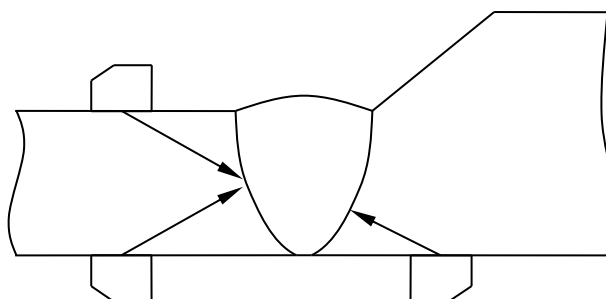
Схема контроля сварных соединений элементов, имеющих скосы кромок
